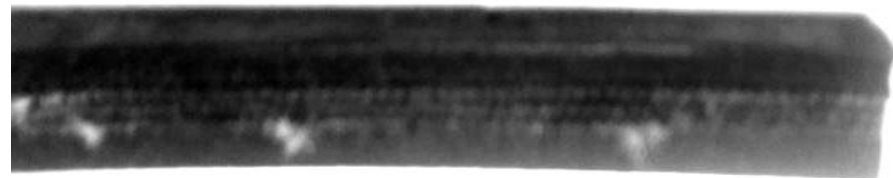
Качество реза резины при резке на фрезерно-отрезном станке
